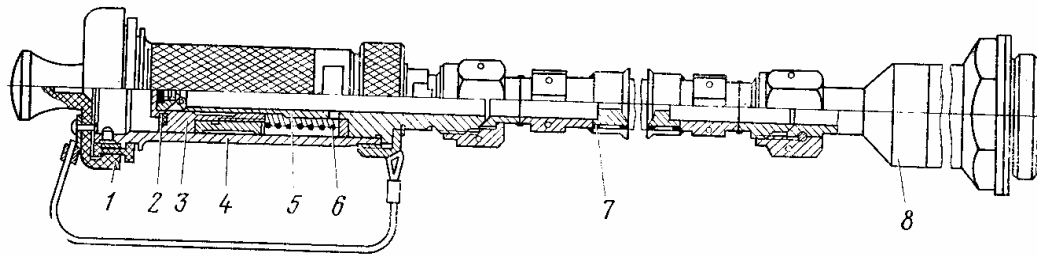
Приспособление 6855-2 для закрытой заправки маслом:
